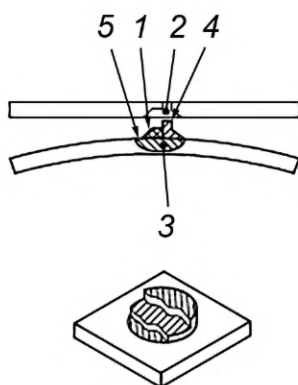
Измерение диаметра сварного шва при частичном разрушении толщины
